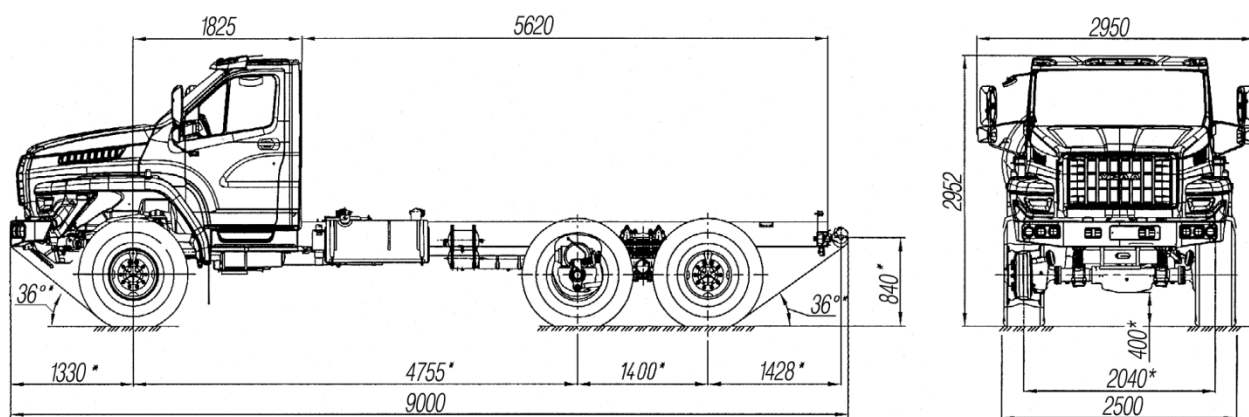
Габаритные размеры шасси Урал-4320-6951-72/74
